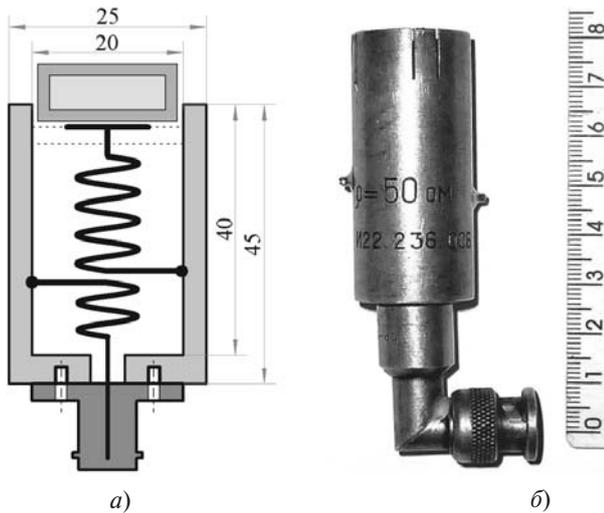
Спиральный резонатор с входным разъемом типа CP-50: а – схема конструкции; б – внешний вид
